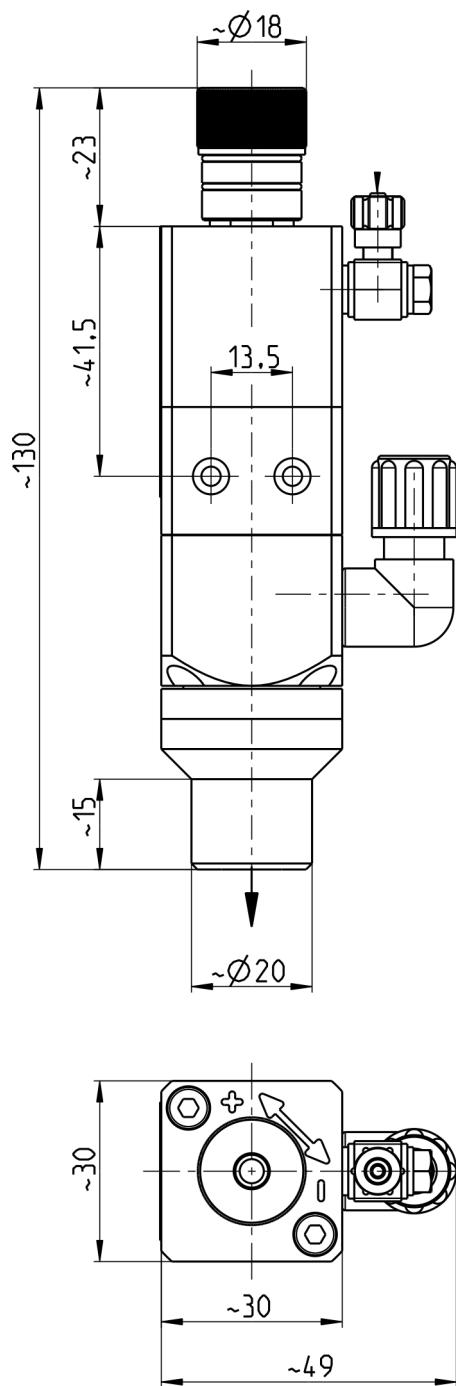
Dimensions de la soupape de dosage EP et EP-FD 295218, 295219, 295223
